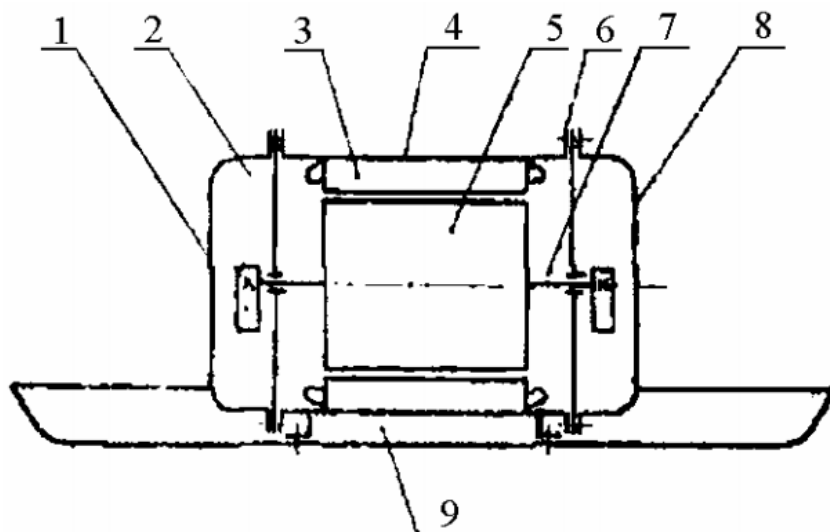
Поверхностный вибратор с круговыми колебаниями
